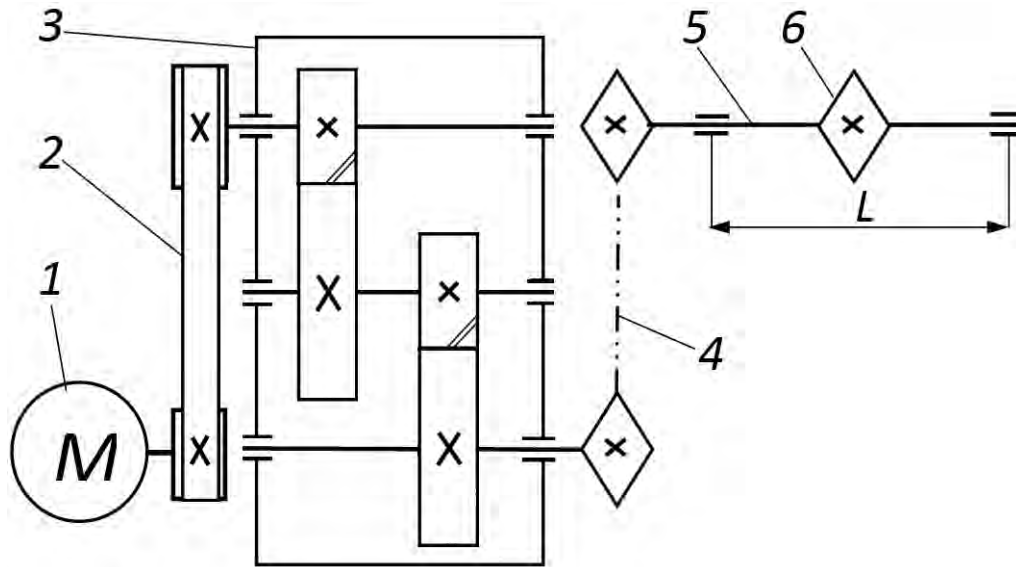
Схема привода скребкового конвейера (вид сверху): 1 – асинхронный электродвигатель; 2 – клиноременная передача; 3 – редуктор двухступенчатый (с цилиндрическими косозубыми передачами); 4 – цепная передача; 5 – приводной вал; 6 – приводная звездочка
